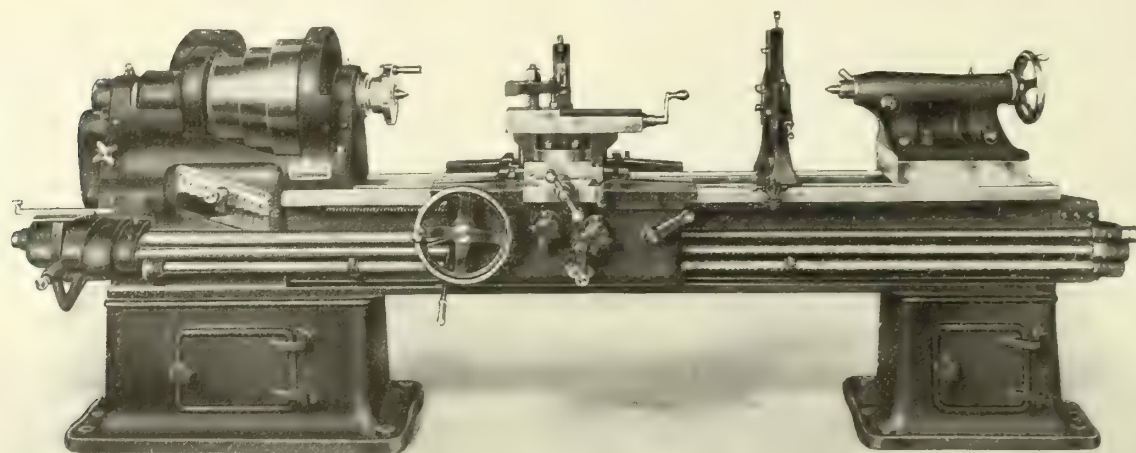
Schnelldrehbank mit Stufenscheiben-Antrieb — 630 mm Drehdurchmesser über dem Bett
